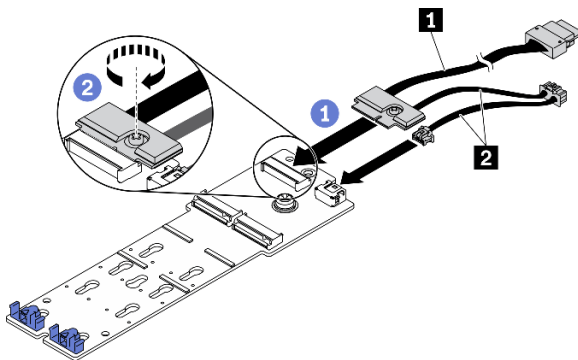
Connexion des câbles du fond de panier M.2 au fond de panier M.2
